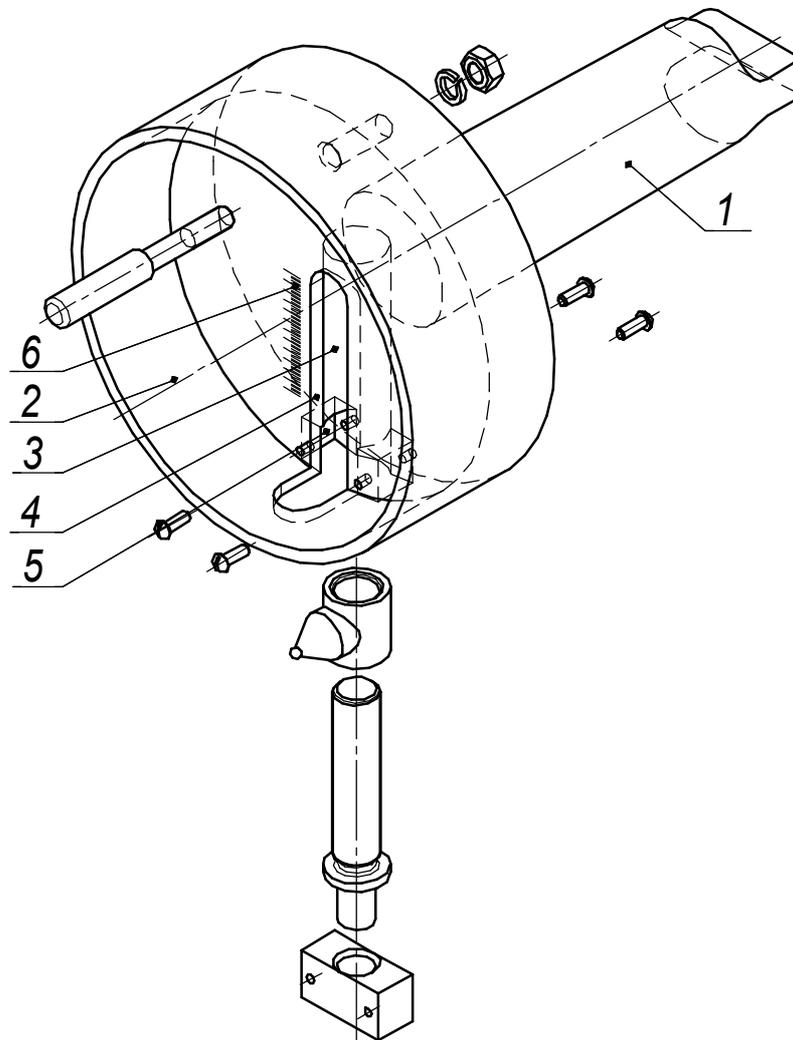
Элементы корпуса смещаемого токарного центра: 1 – хвостовик; 2 – защитный кожух; 3 – направляющее отверстие; 4 – направляющий паз; 5 – паз под втулку; 6 – шкала
